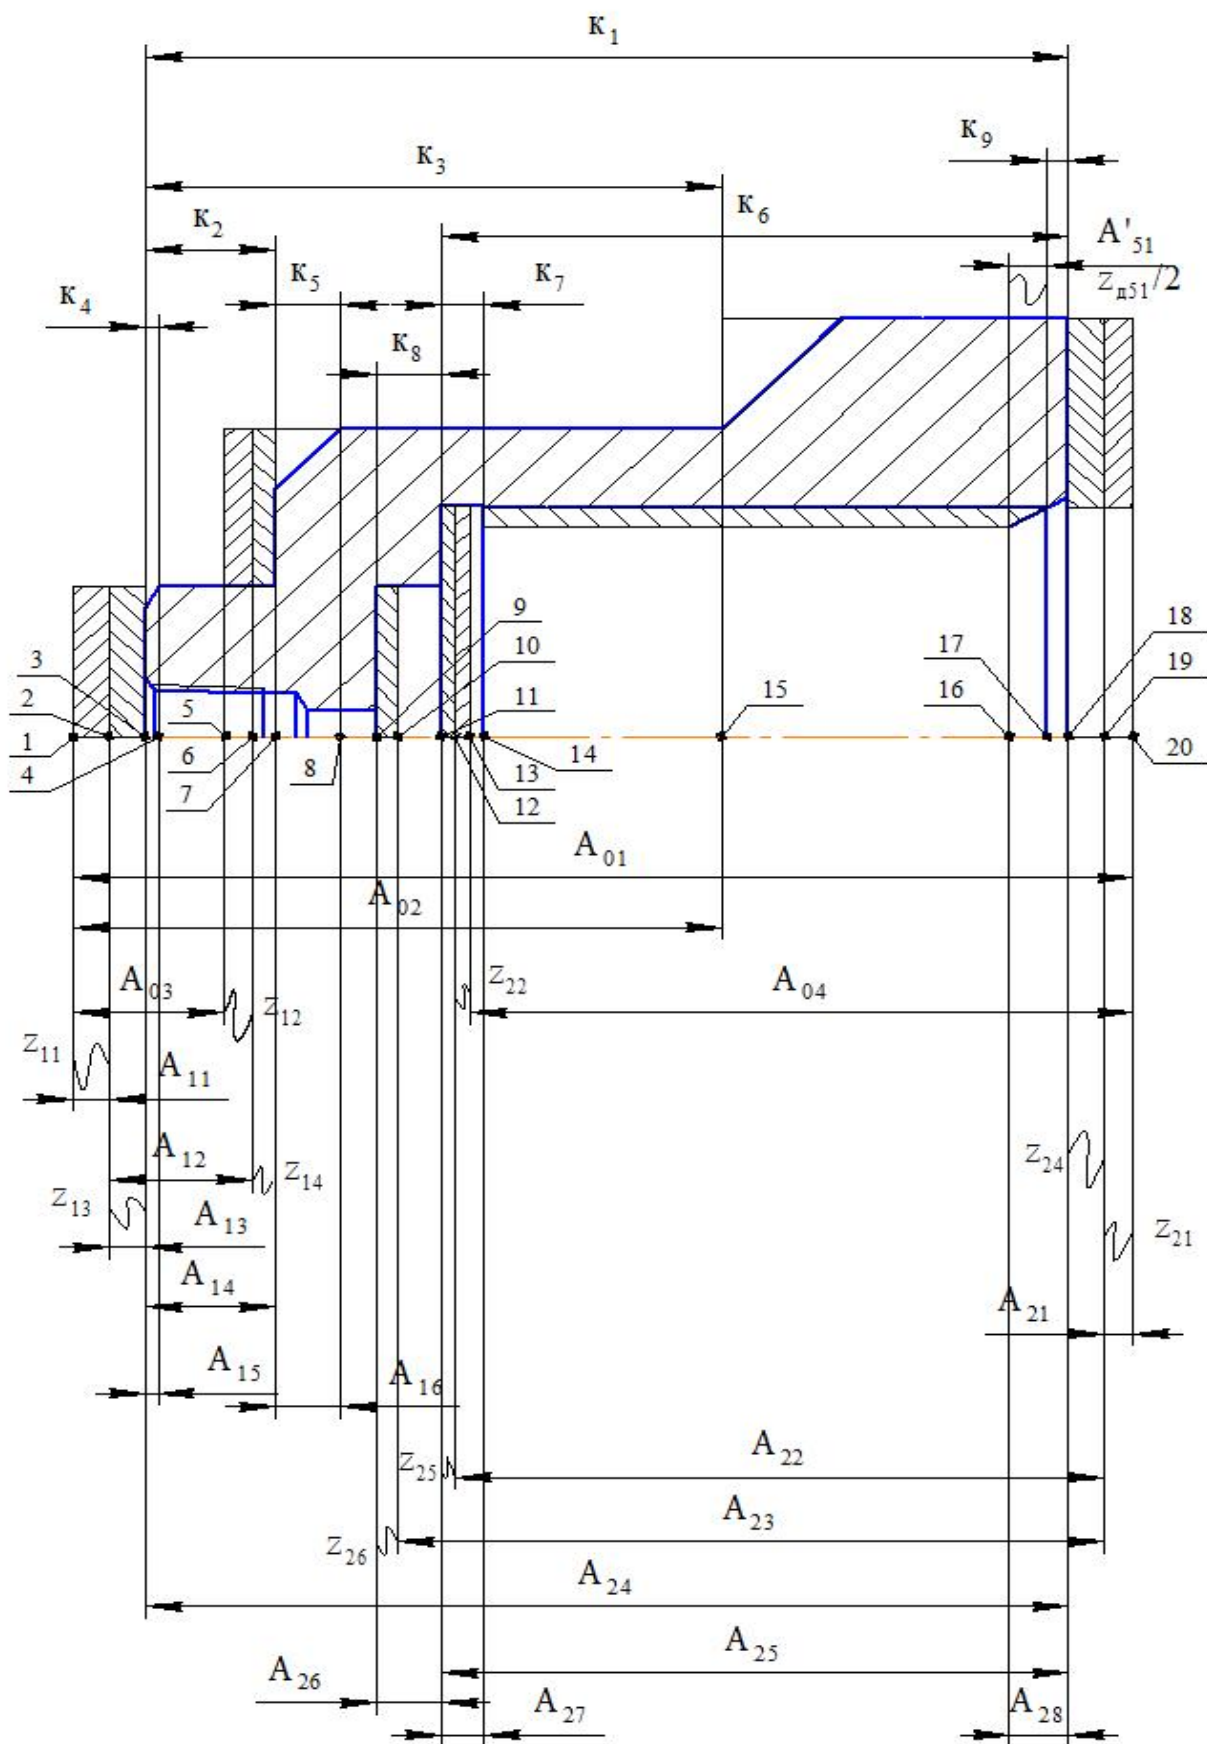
Размерная схема технологического процесса изготовления детали «Корпус» (продольное направление).
